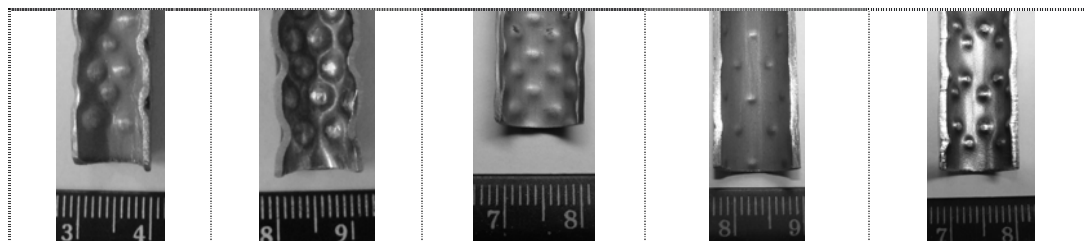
Фотографии профилей сечения труб с полусферическими выступами (3D-шероховатость)
